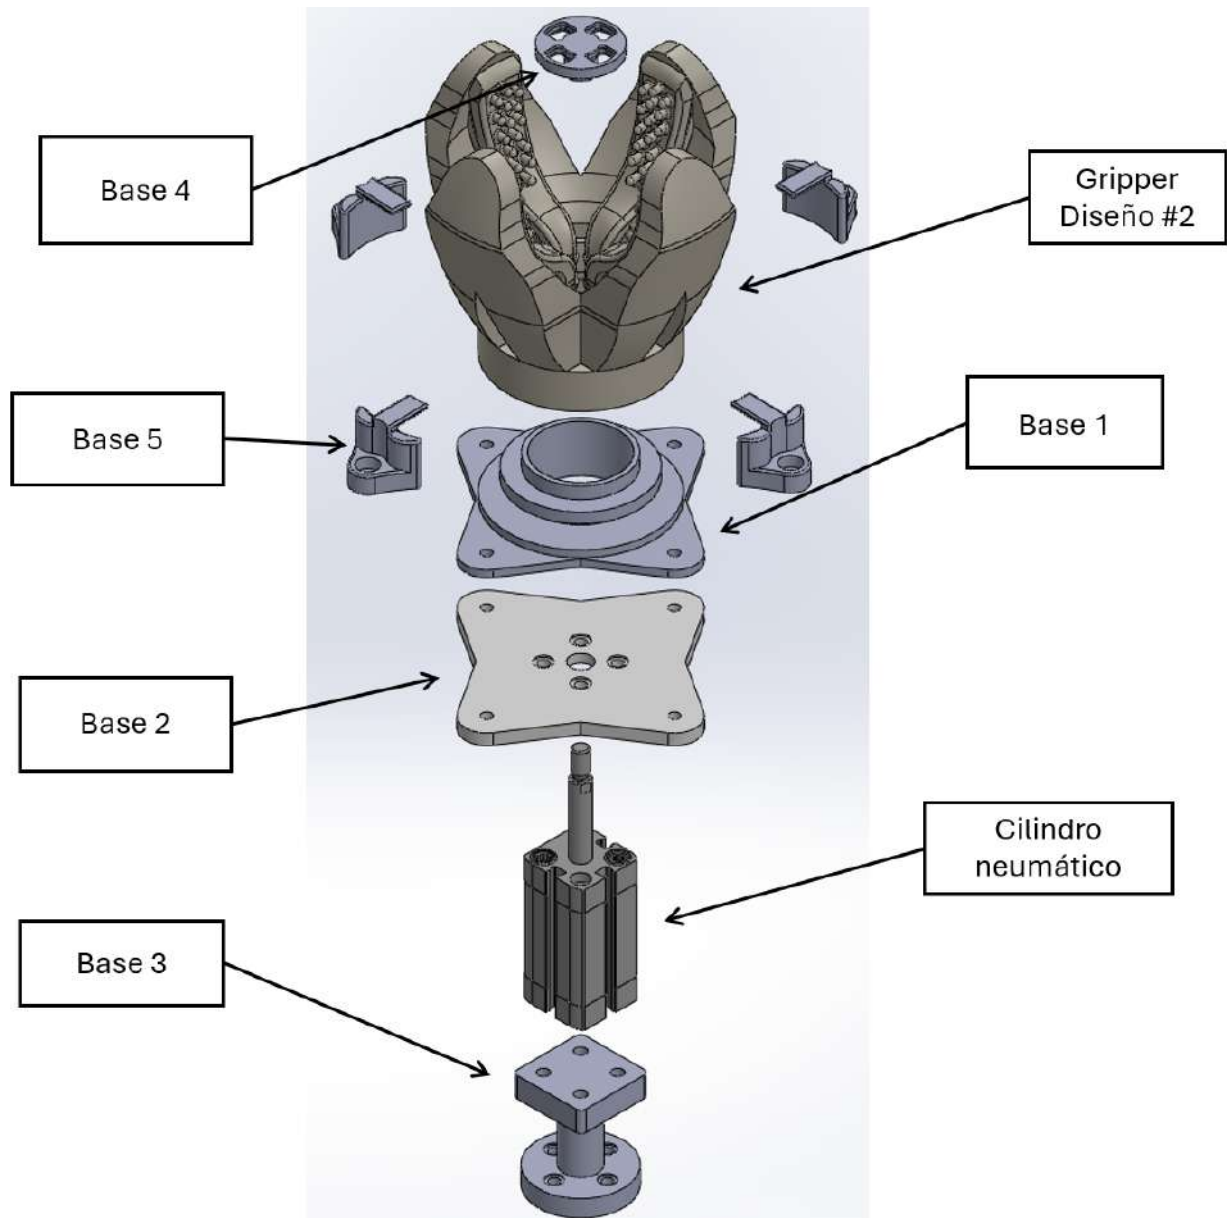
Vista explosionada de la base en el ensamble final del gripper.
